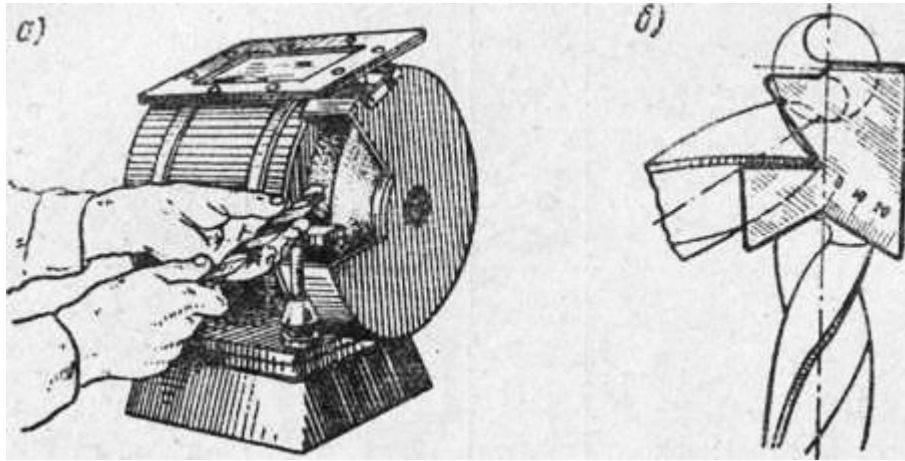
заточка свердла(а); перевірка кутів заточування свердла шаблоном (б)
